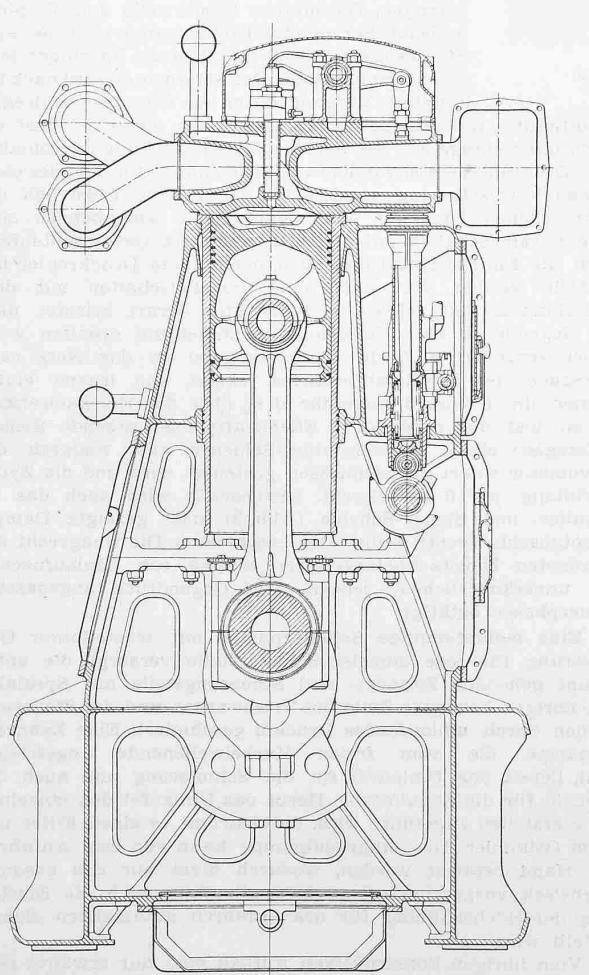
Schnitt durch einen einfach wirkenden Sulzer-Viertakt-Lokomotivmotor mit Zylinderblock und Kurbelgehäuse in geschweisster Ausführung
